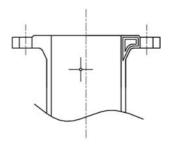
有铸孔冷却热节 Fig. 13 The cooling hot spot with casting hole
